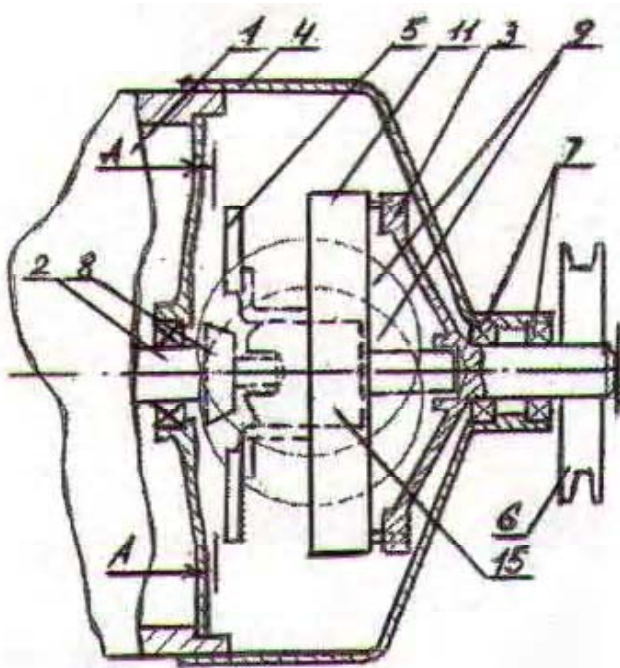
Конструктивная схема приводного устройства для стартер-генератора:
